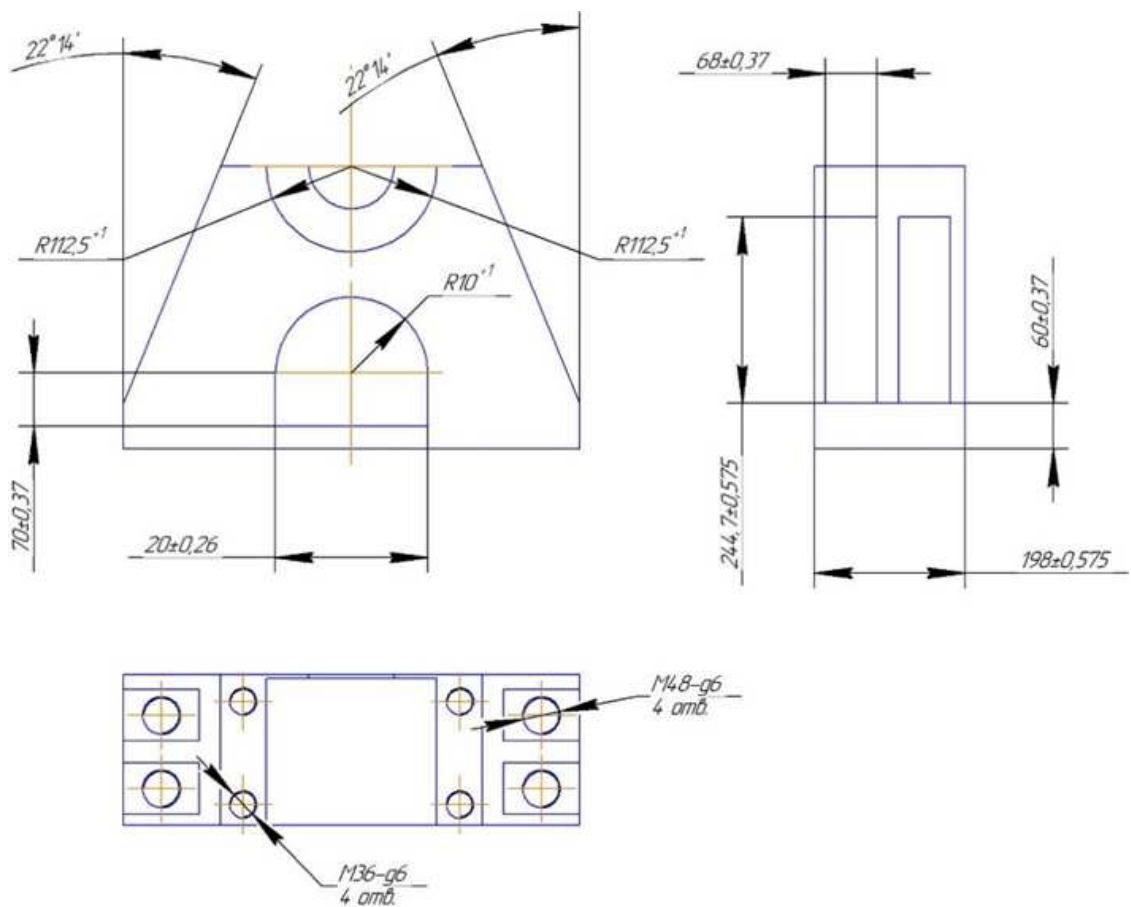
Нижня частина корпусу для кріплення підшипників.
